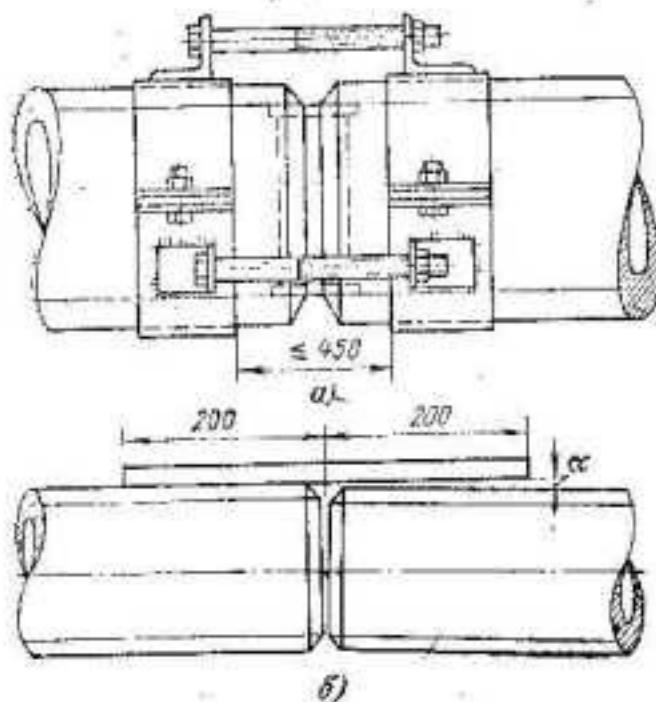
Проверка прямолинейности труб при сборке стыков под сварку.
